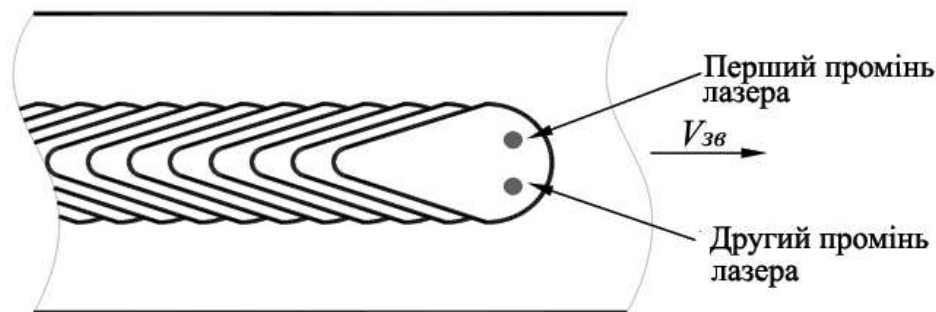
Лазерне зварювання двома паралельними променями лазера
